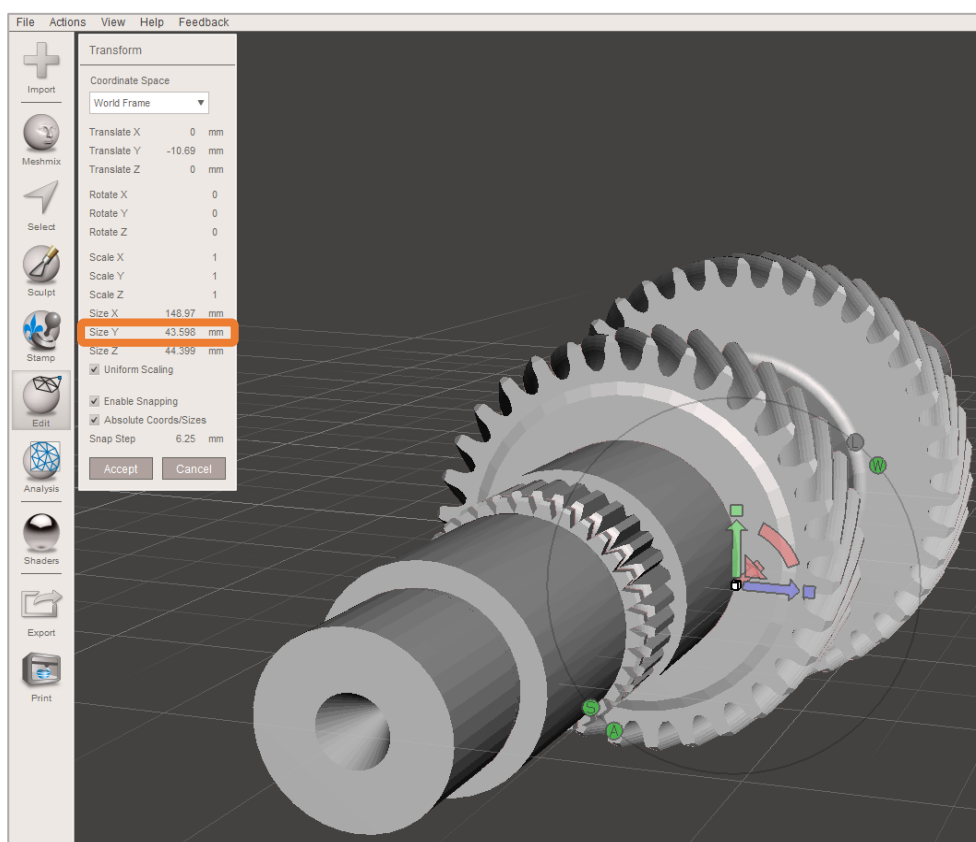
34 Modificación realizada sobre el archivo EJE SECUNDARIO
